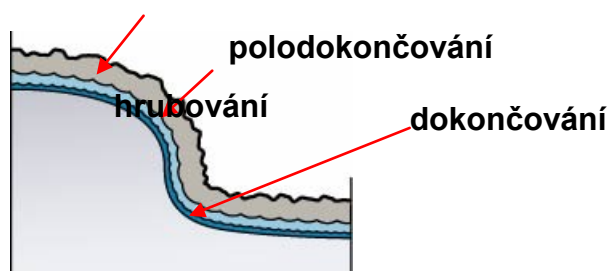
Typické příklady obrábění tvaru kulovou frézou [2]
